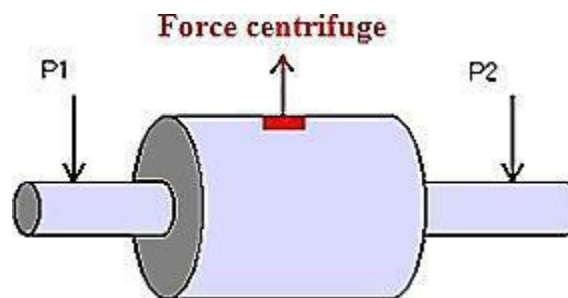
Tolérances d'usinage sur un rotor. [19]
